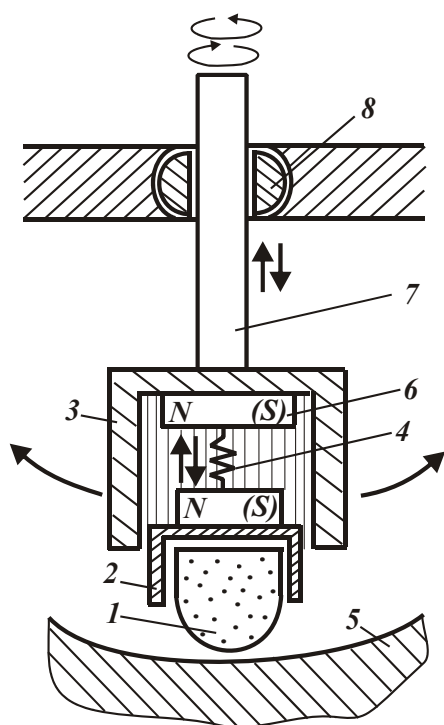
Телескопическое шлифовальное устройство для обработки больших эллипсно-сферических поверхностей по контуру: 1 – шлифовальный круг; 2 – патрон для шлифовального круга с электромагнитом; 3 – направляющий цилиндр со шлицами, по которому перемещается патрон со шлицами; 4 – пружина подвески патрона со шлифовальным кругом; 5 – обрабатываемая деталь; 6 – электромагнит; 7 – вал; 8 – шаровая подвеска – сферическое соединение.
